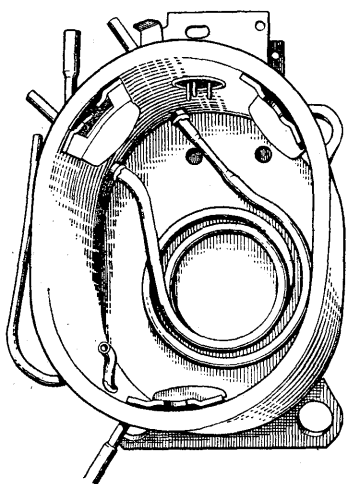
Расположение маслоохладителя в кожухе компрессора.
